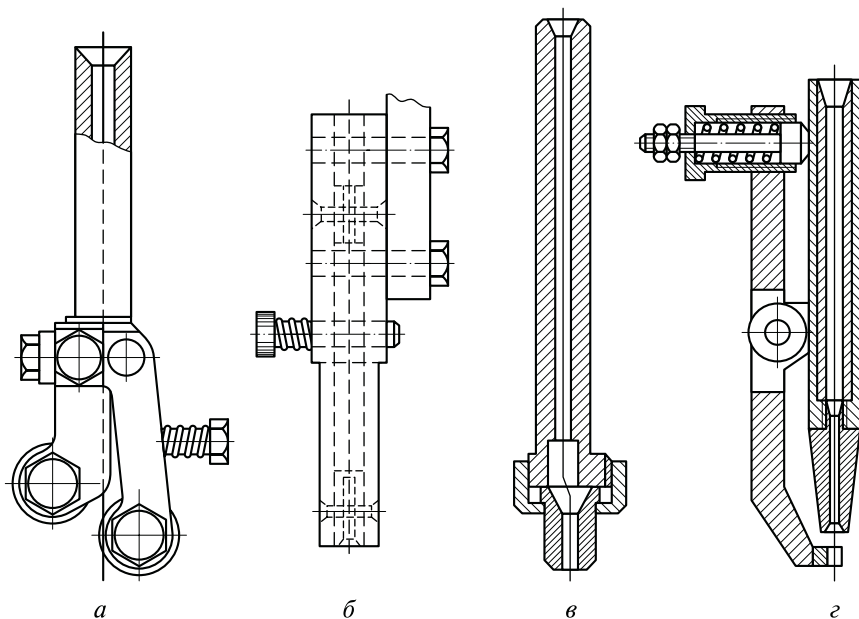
Токоподводящие мундштуки для сварочных автоматов:
